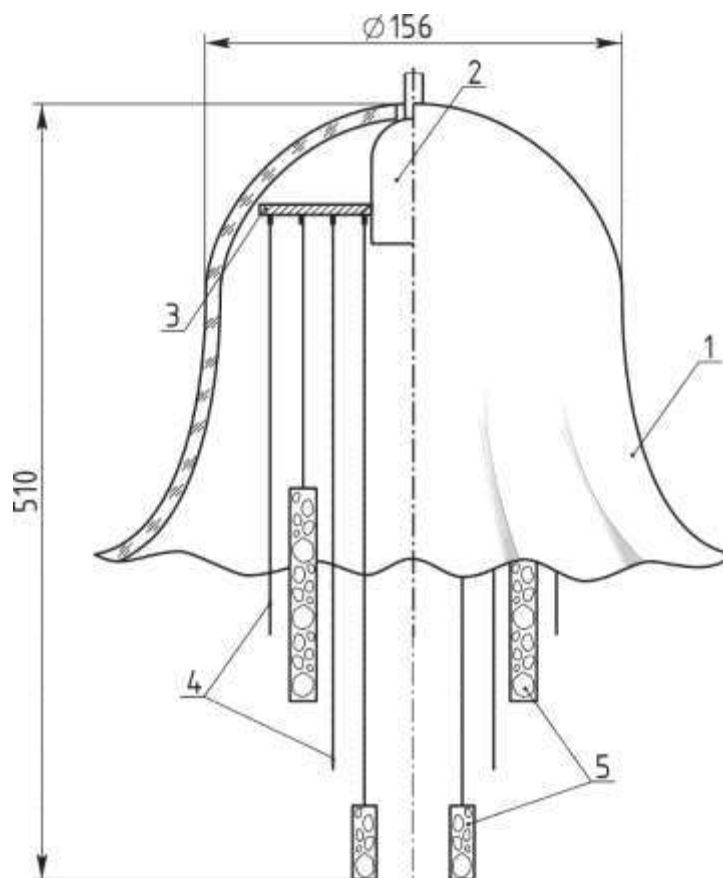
Конструктивная схема плафона в сборе: 1- корпус, 2 – патрон, 3 – диск, 4 – цепочки, 5- декоративные пластинки
